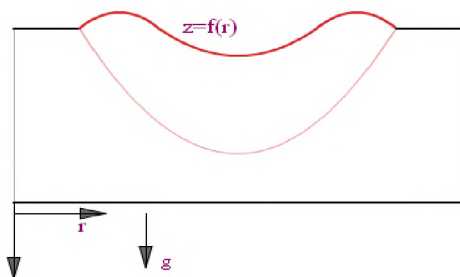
Схематическое представление деформации поверхности сварочной
